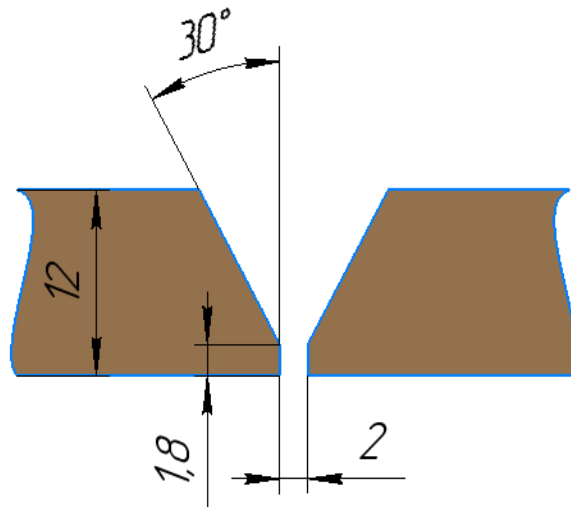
Подготовка кромок стыка трубы при сварке нефтепровода
